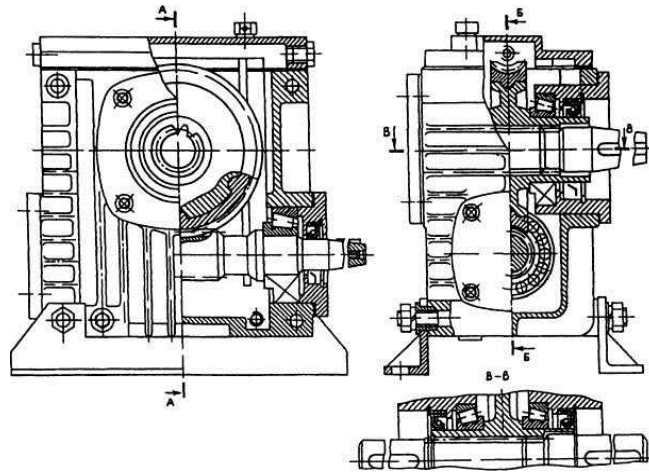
Одноступенчатый червячный редуктор с универсальным корпусом
